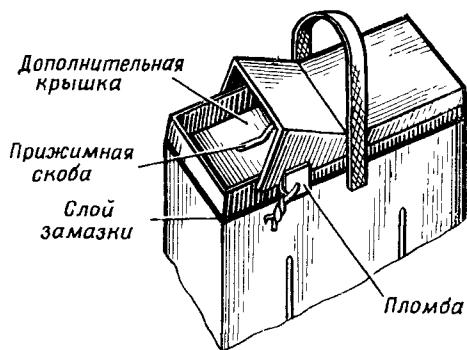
Общий вид коробки с патронами в лентах с постановкой дополнительной крышки и промазкой стыка крышки с корпусом коробки замазкой ЗЗК-3У
